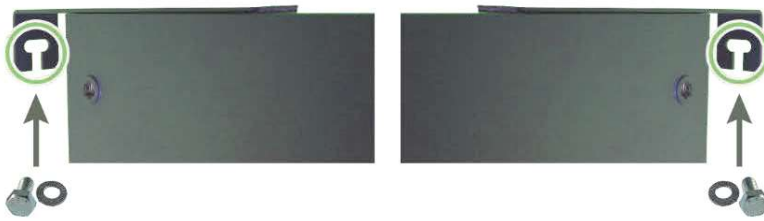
Kippschutzbügel an der Montagewand befestigen
